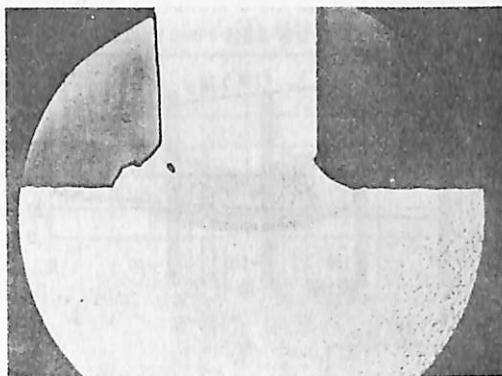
ASTM 304L Steel Bolts Stud Welded to ABS-CS Steel
